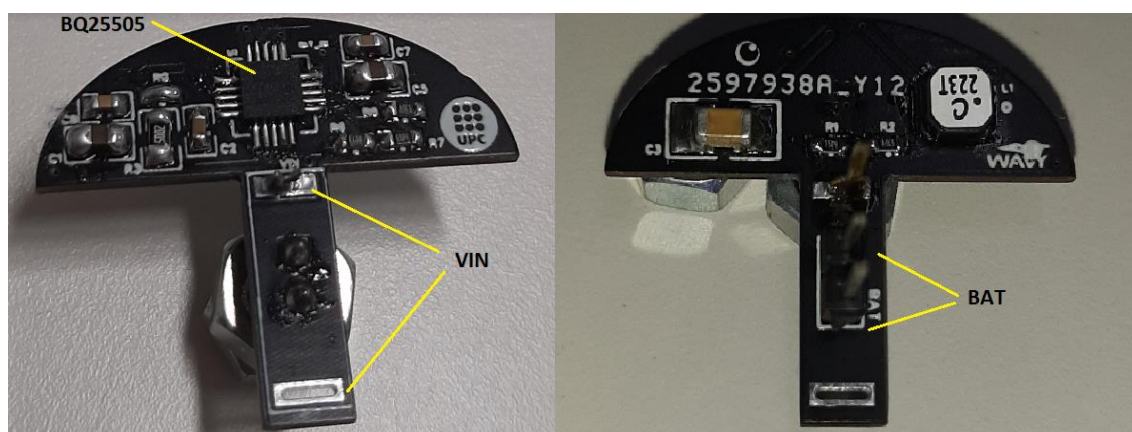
Aspecto de la placa BQ25505-DL tras realizar la soldadura de sus componentes.
